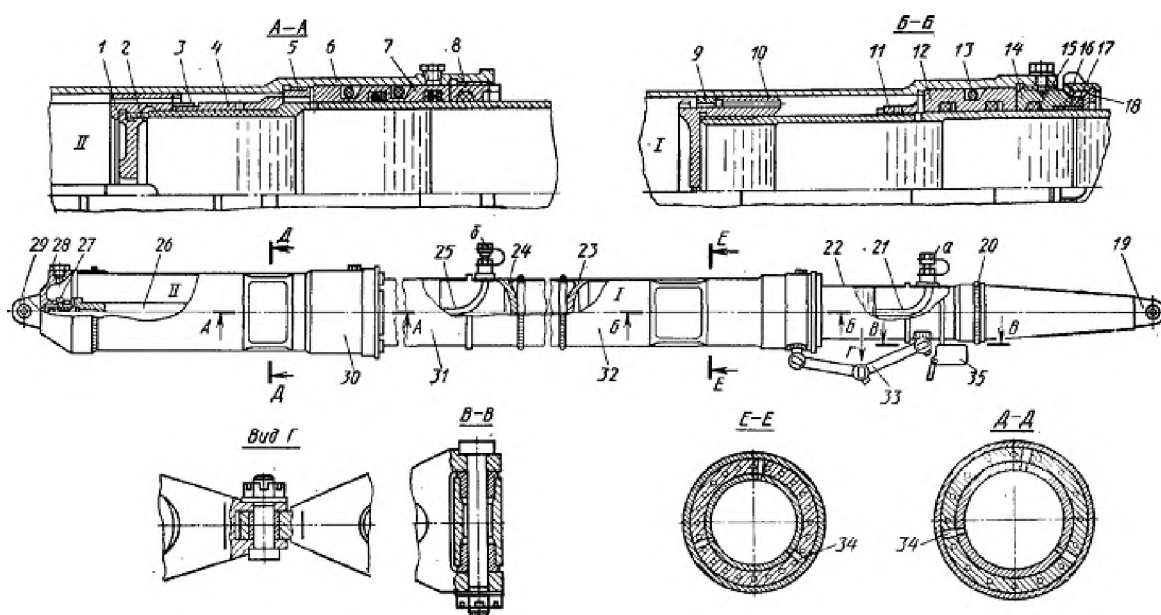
Конструкция двухкамерного амортизатора главной стойки шасси Ми-17 [15]:
